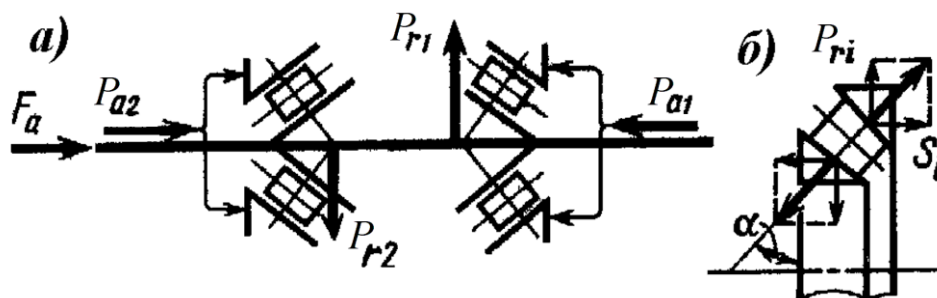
Схема к определению сил, действующих на радиально-упорные подшипники
